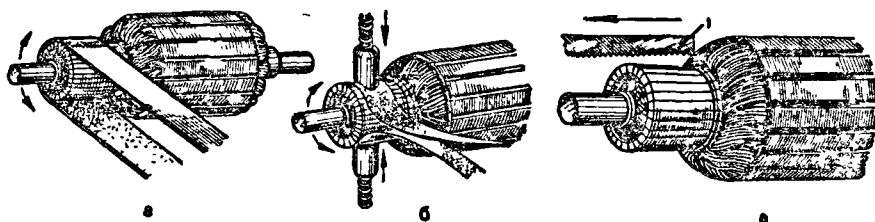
Обслуживание генератора: а — шлифовка коллектора шкуркой; б — притирка щеток, в — очистка пластин: 1 — ножовочное полотно
